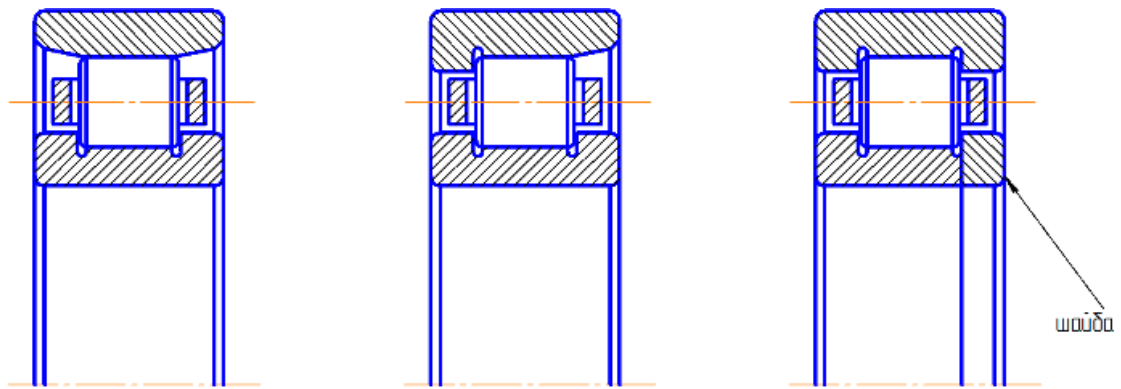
Конструкція роликів однорядного підшипника
